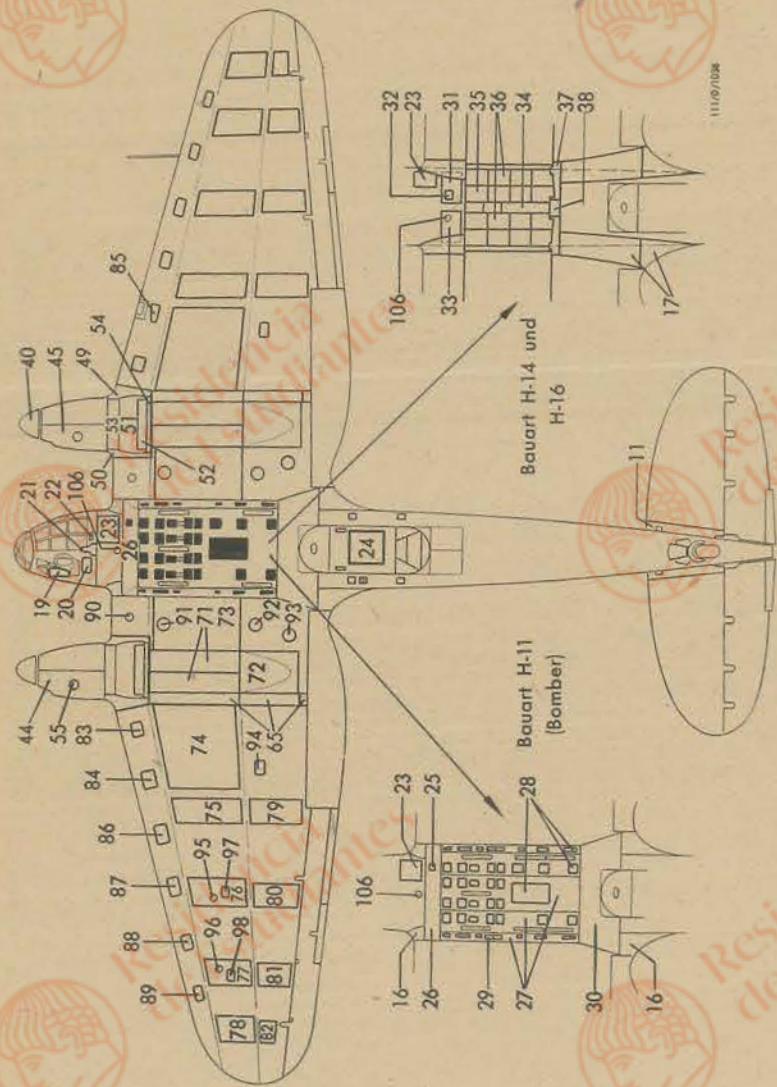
Deckel- und Klappenplan (Ansicht von unten)
